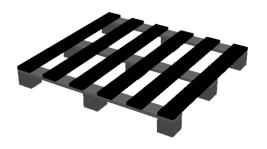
托盘不可移动部分 Fig.2 Immovable part arrangement of the pallet
